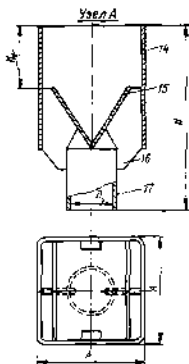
Установка ГП с приспособлением для его настройки.
